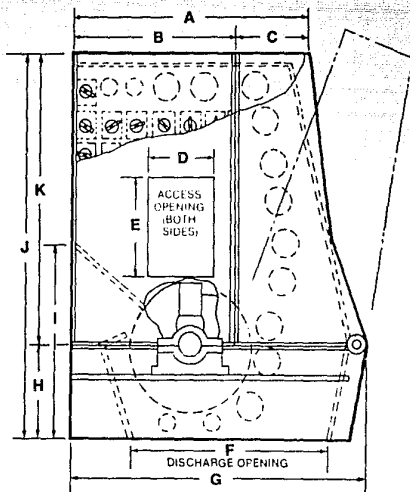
CORTE DE UNA TRITURADORA DE IMPACTO DE SIMPLE ROTOR
